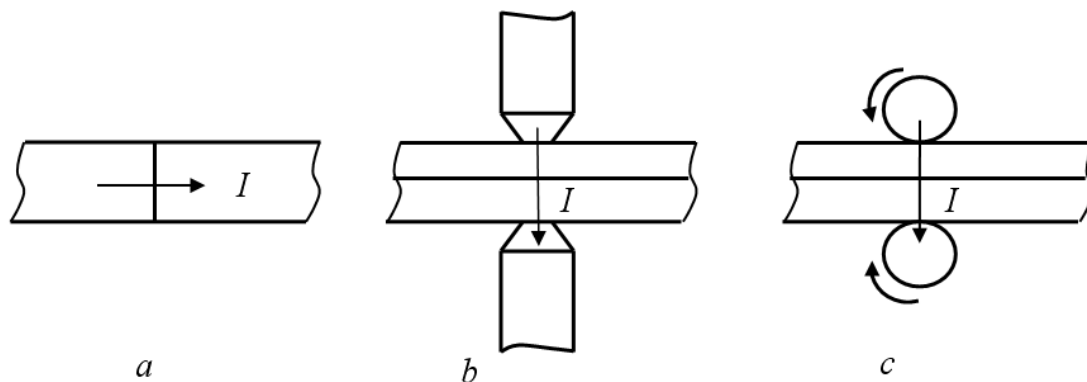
Moyens principaux de soudage par contacts :
